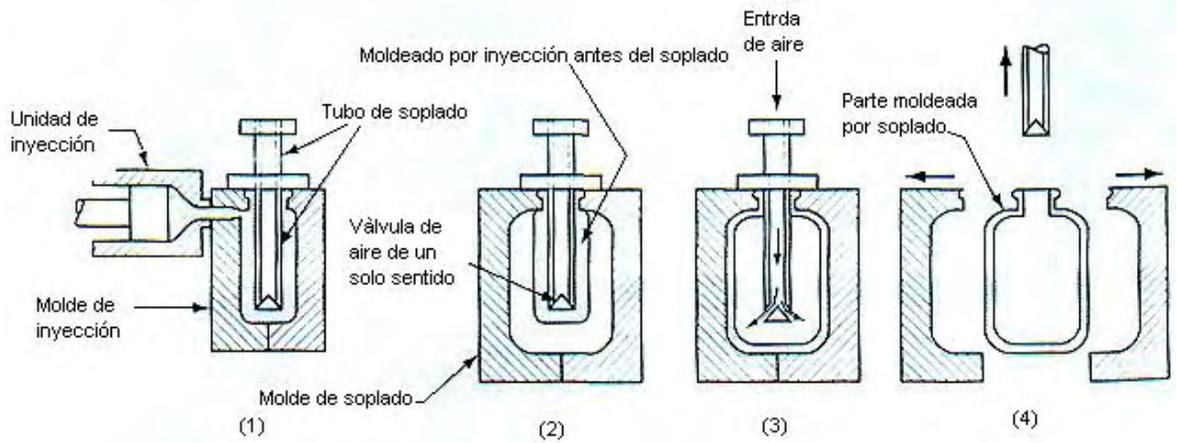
Técnica 1. Moldeo por inyección y soplado (51)
